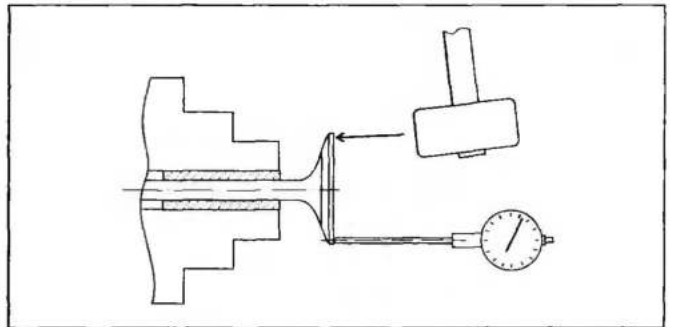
Схема правки тарелки клапана в патроне токарного станка
